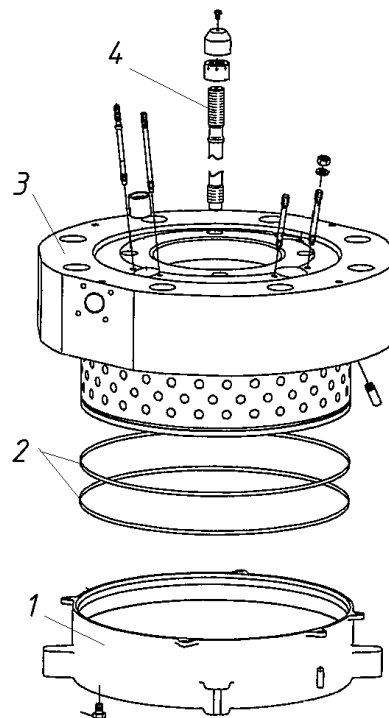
Кришка циліндру [2]. 1 – сорочка охолодження; 2 – резинові ущільнювачі; 3 – кришка; 4 – шпильки кріплення клапанного вузла
